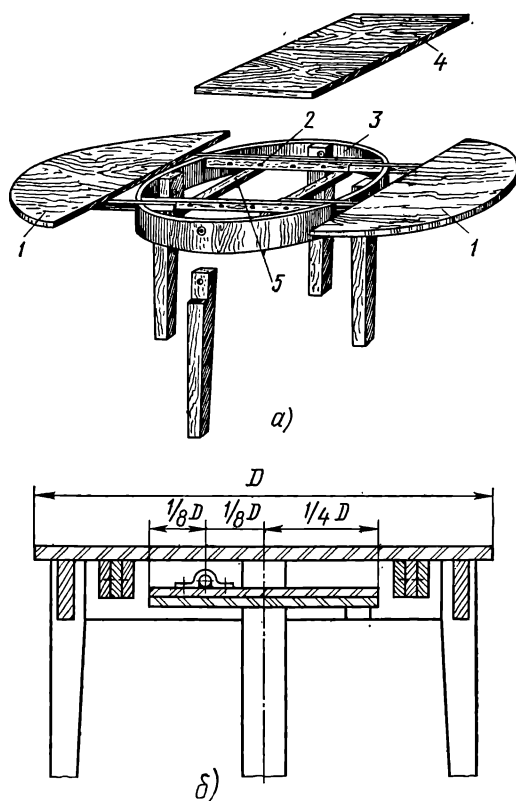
Конструкция стола с раздвижными крышками и нераздвижной круглой царгой:
